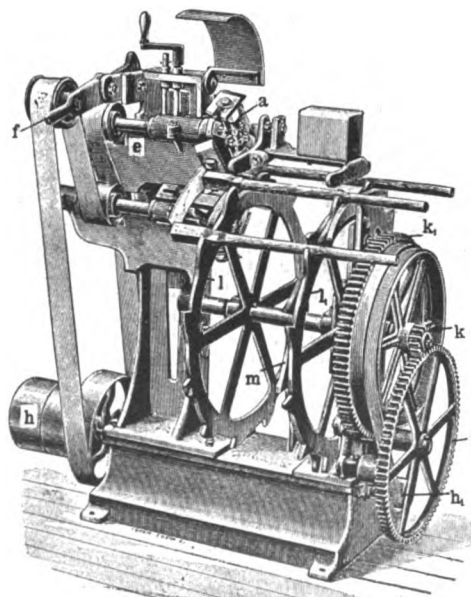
Zapfenschneidmaschine mit zwei Messerköpfen.
